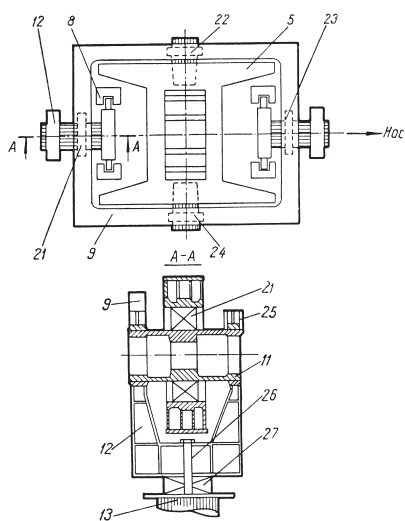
Расположение подшипников качения в карданном подвесе (вид сверху): поз. 5–20 — те же, что и на рис. 5 и 6; 21 — кормовой подшипник; 22 — подшипник левого борта; 23 — носовой подшипник; 25 — стопорный наколенчик вилки; 26 — крепеж вилки; 27 — подушка, опоры вилки
